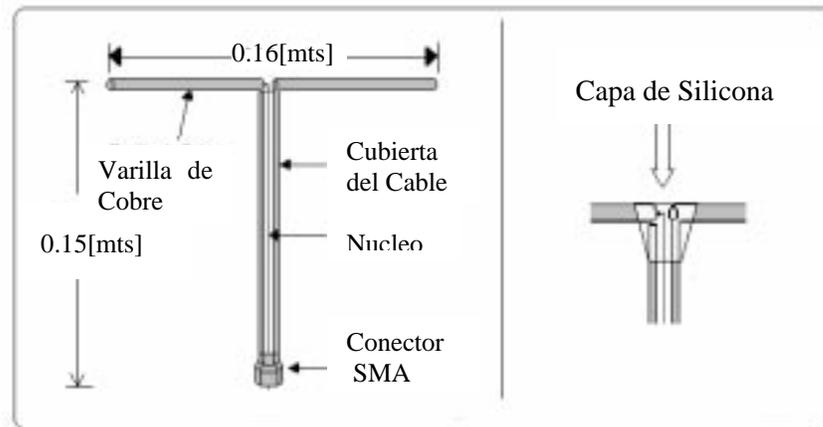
Dibujo del dipolo, componentes y dimensiones.
